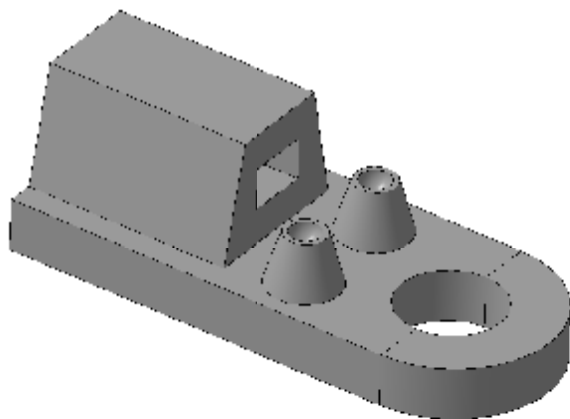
Аксонометрическое изображение детали «Корпус защелки»
